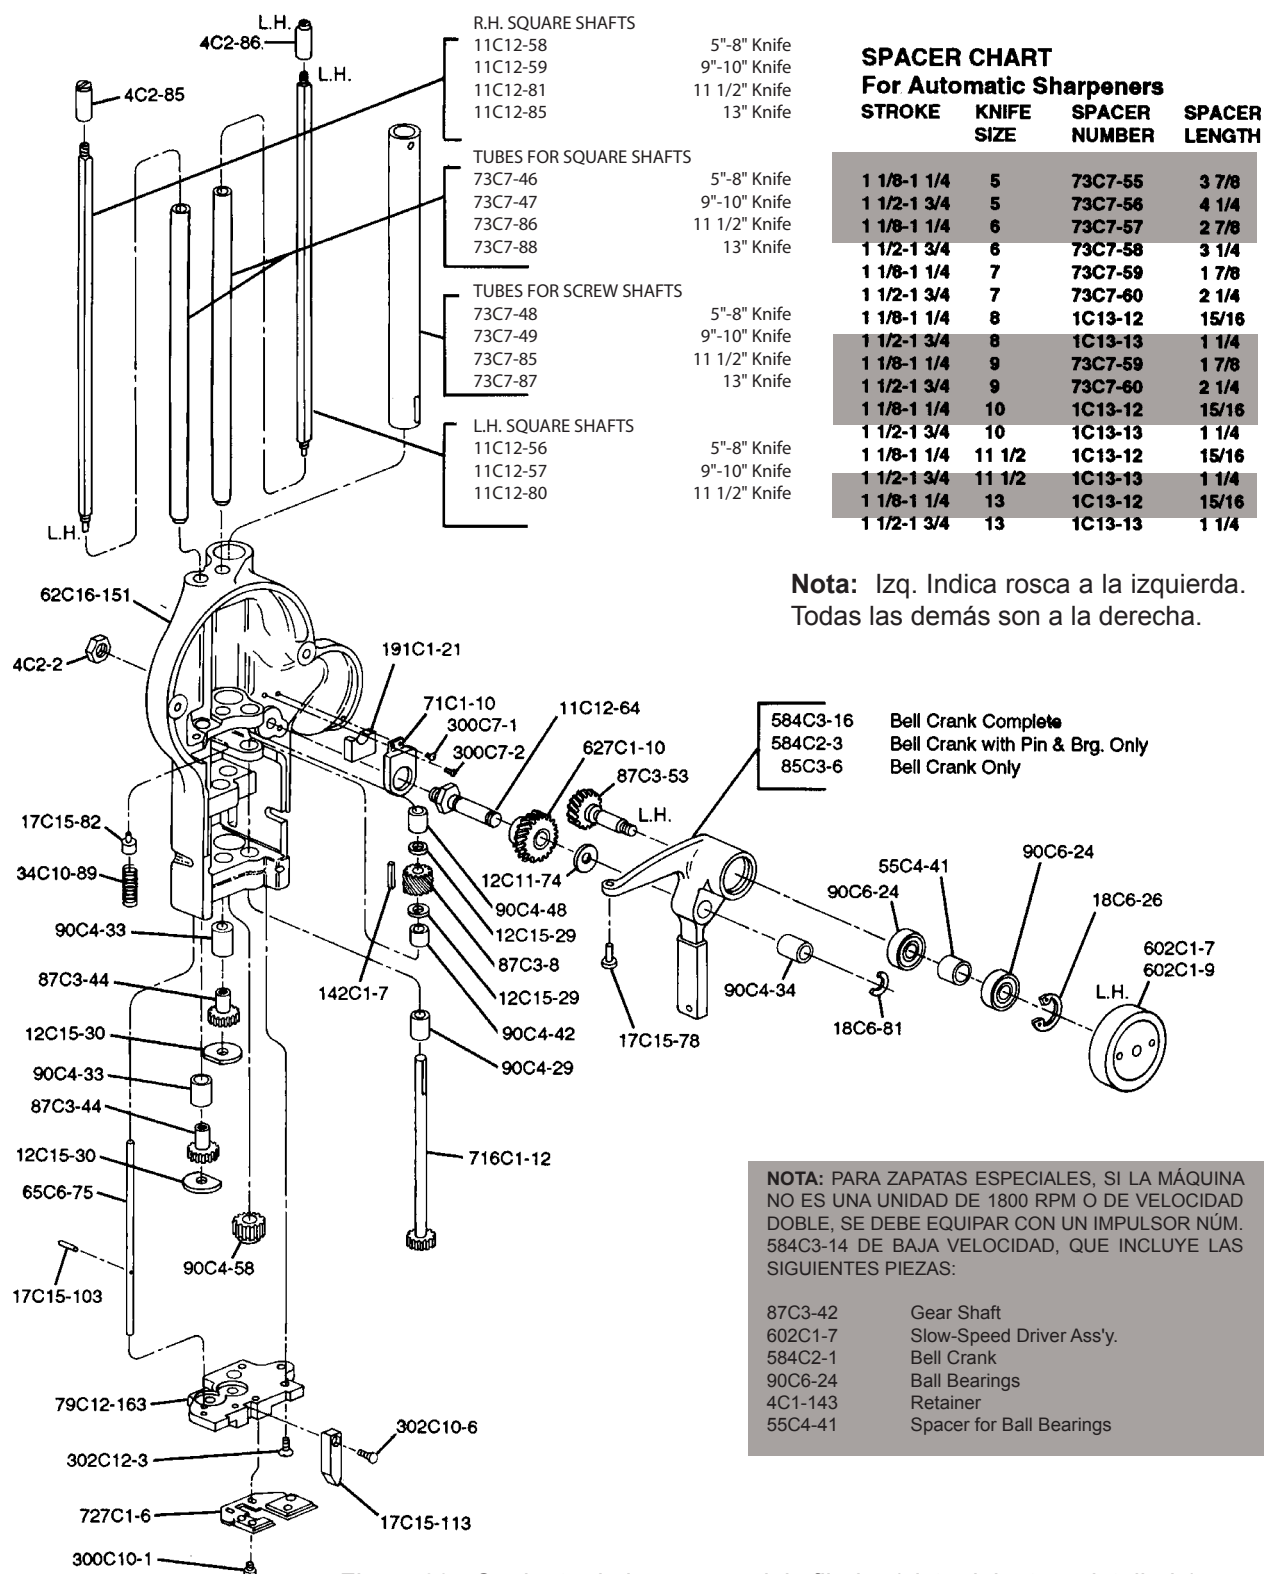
Conjunto de la carcasa del afilador (vista delantera detallada)
